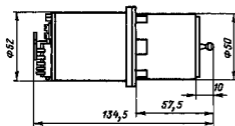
24 Габаритные и установочные размеры двигатель-тахогенератора АДТ-524, АДТ-534
